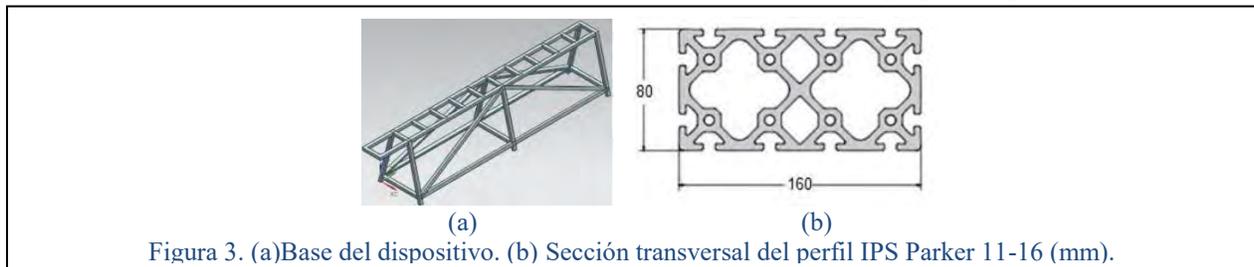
(a) Base del dispositivo. (b) Sección transversal del perfil IPS Parker 11-16 (mm).
